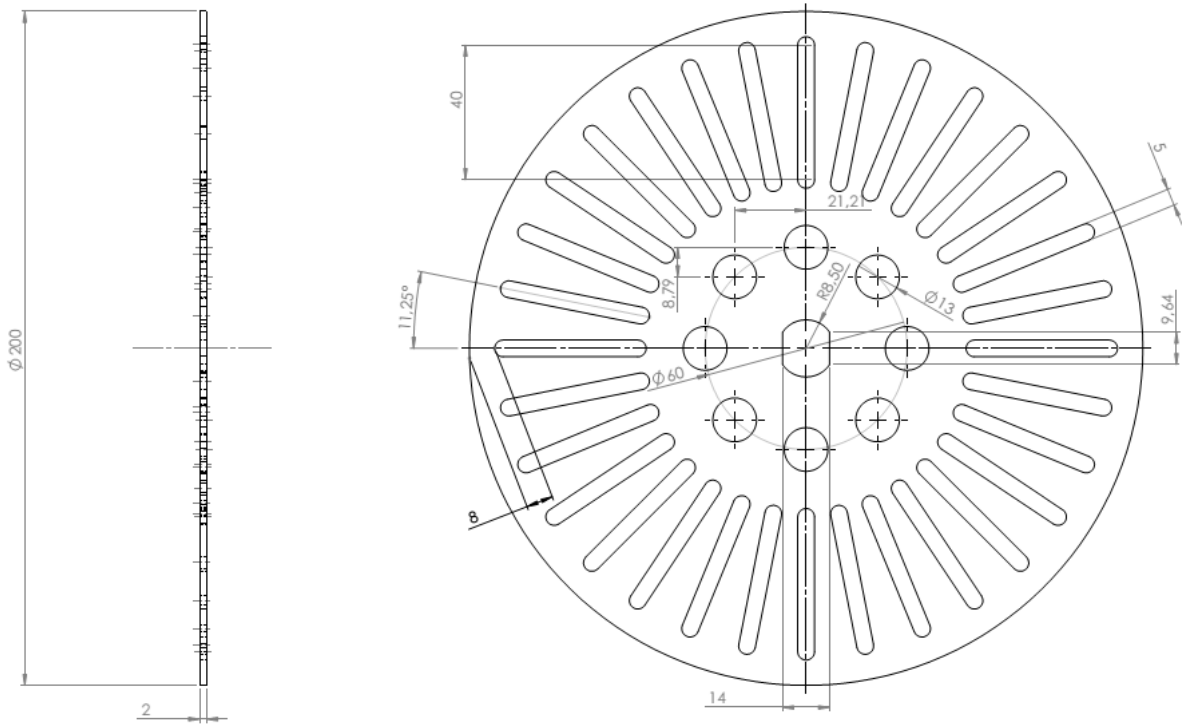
Dimensões (em milímetros) dos discos do rotor tipo G.
